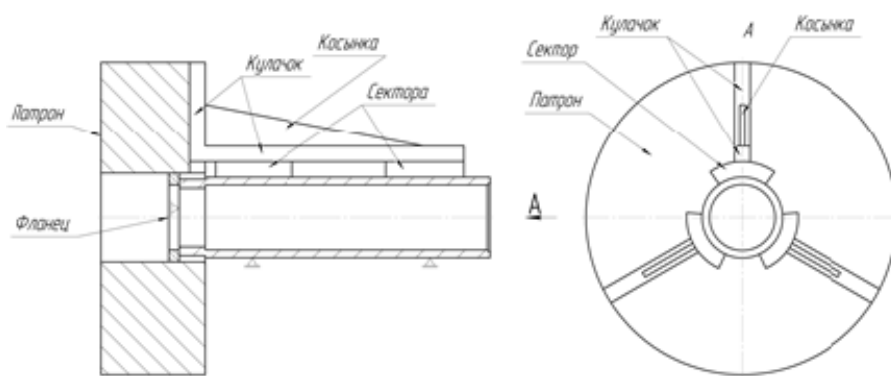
Схема установки для механической обработки головных и хвостовых труб
